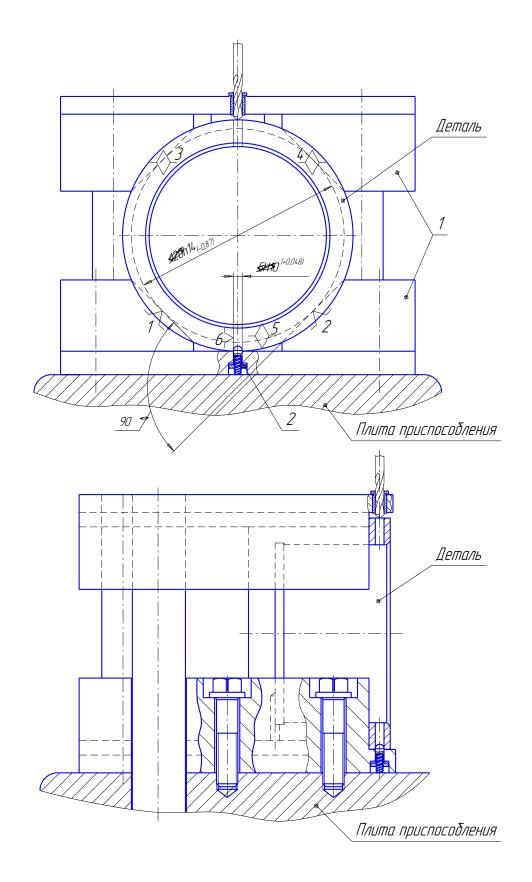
Схема базирования заготовки (цилиндр) с установочными элементами приспособления: 1. призмы; 2. палец подпружиненный
